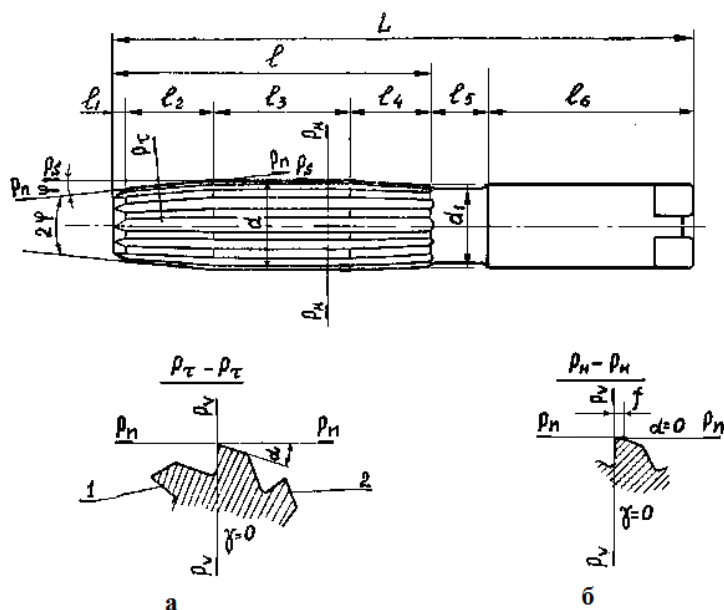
Элементы и геометрия ручной хвостовой развертки
